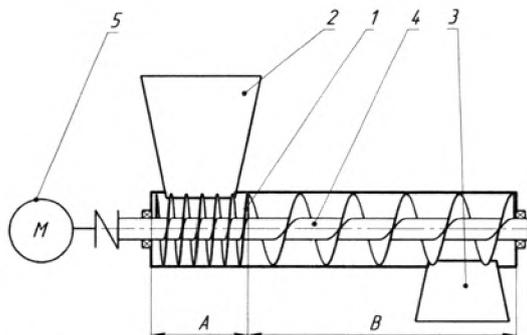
Винтовой конвейер: 1 – цилиндрический кожух, 2 – загрузочное устройство, 3 – разгрузочное устройство, 4 – винт, 5 – мотор-редуктор
